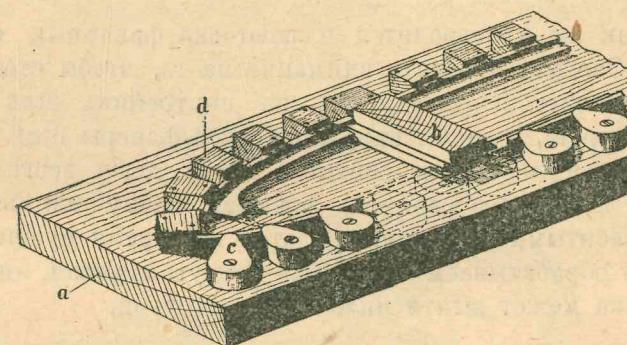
Стенки нервюр, шаблоны для пригонки заготовки.
